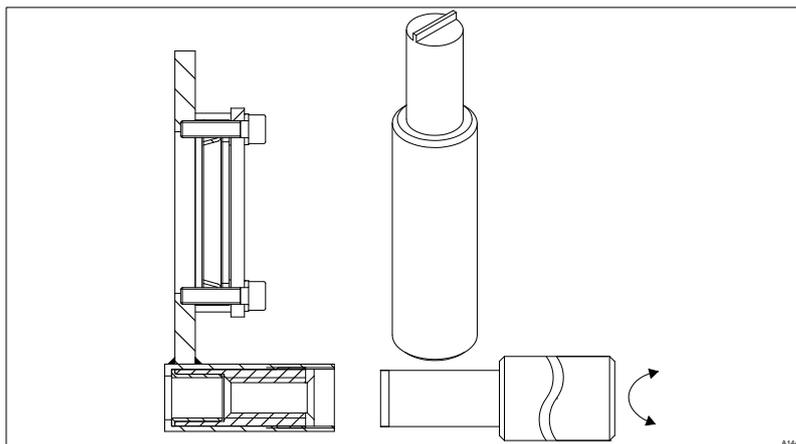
Werkzeug für die Gewindehülse in der Wischeraufnahme, Teilenummer 1037738
